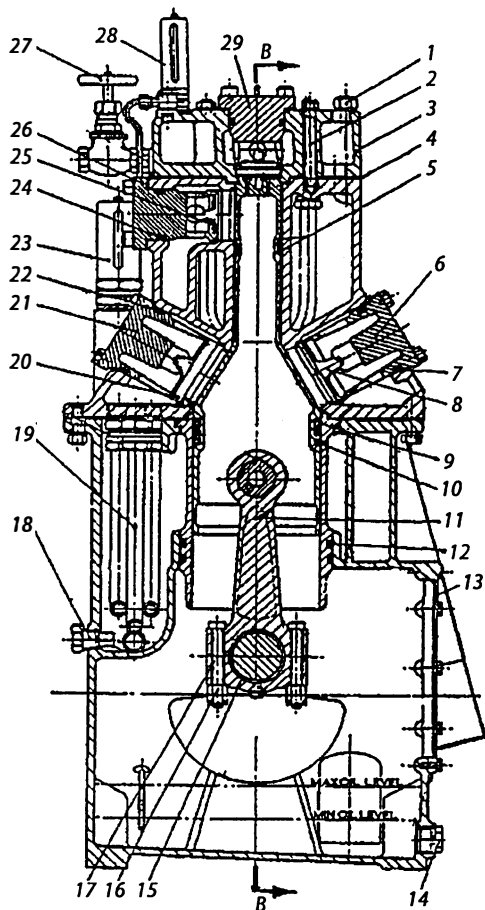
Воздушный компрессор 2SF4 (разрез А—А): 1 — гайка, 2 — шпилька, 3 — головка цилиндра второй ступени, 4 — прокладка, 5 — компрессионное кольцо второй ступени, 6 — корпус всасывающего клапана первой ступени, 7 — уплотнительное кольцо, 8 — всасывающий клапан первой ступени, 9 — компрессионное кольцо первой ступени, 10 — маслоъемное кольцо, 11 — шатун, 12 — уплотнительное кольцо, 13 — картер, 14 — пробка спускная, 15 — вкладыш, 16 — гайка, 17 — болт мотылевый, 18 — пробка (анод), 19 — охладитель первой ступени, 20 — нагнетательный клапан первой ступени, 21 — корпус нагнетательного клапана первой ступени, 22 — уплотнительное кольцо, 23 — предохранительный клапан первой ступени, 24 — уплотнительное кольцо, 25 — всасывающий клапан второй ступени, 26 — корпус всасывающего клапана второй ступени, 27 — выпускной вентиль, 28 — предохранительный клапан второй ступени, 29 — корпус нагнетательного клапана второй ступени
